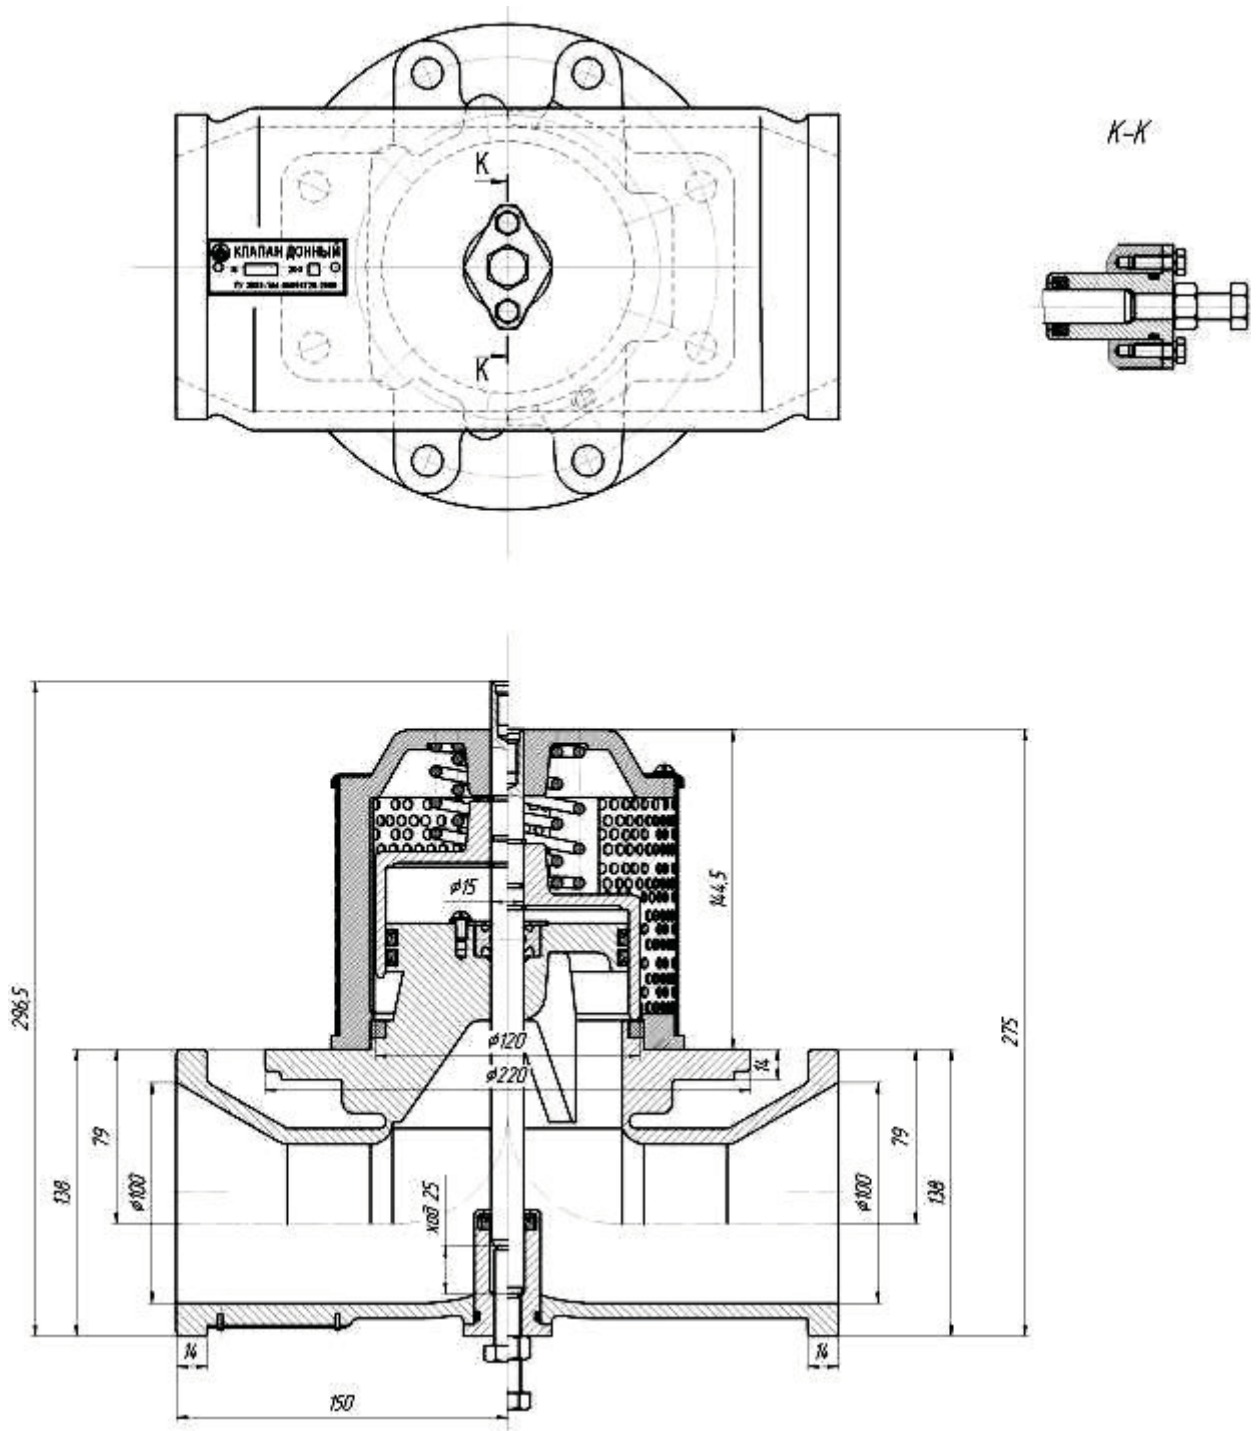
Типовой представитель: клапан донный пневматический Т-образный низкий профиль с ручным дублированием
